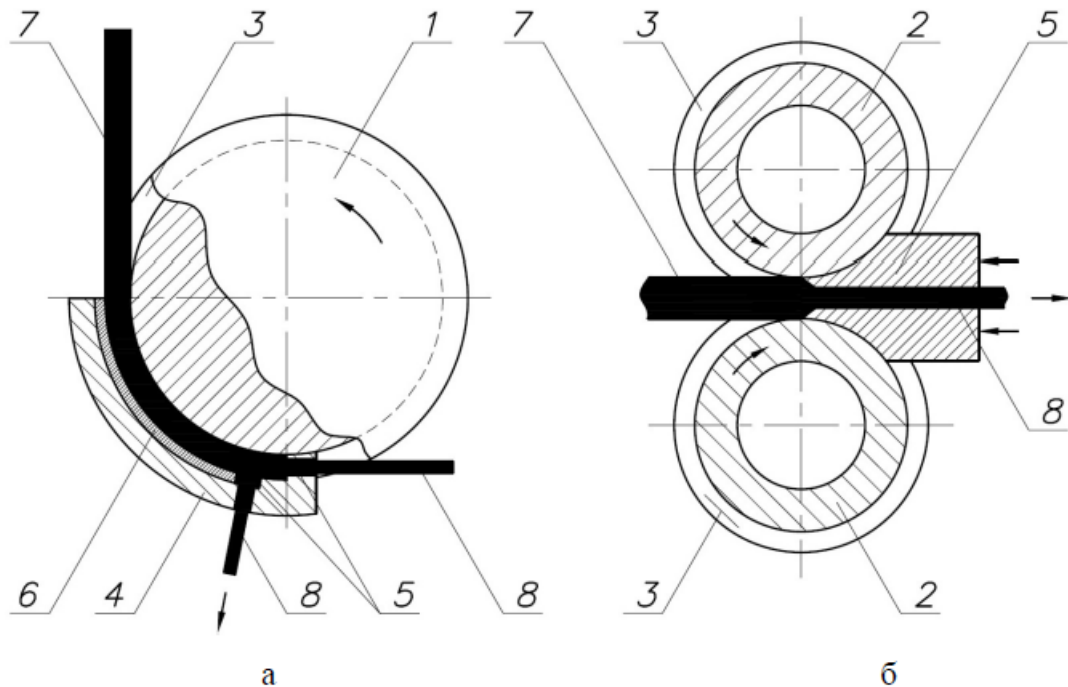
Схемы непрерывного прессования: а) Конформ; б)
